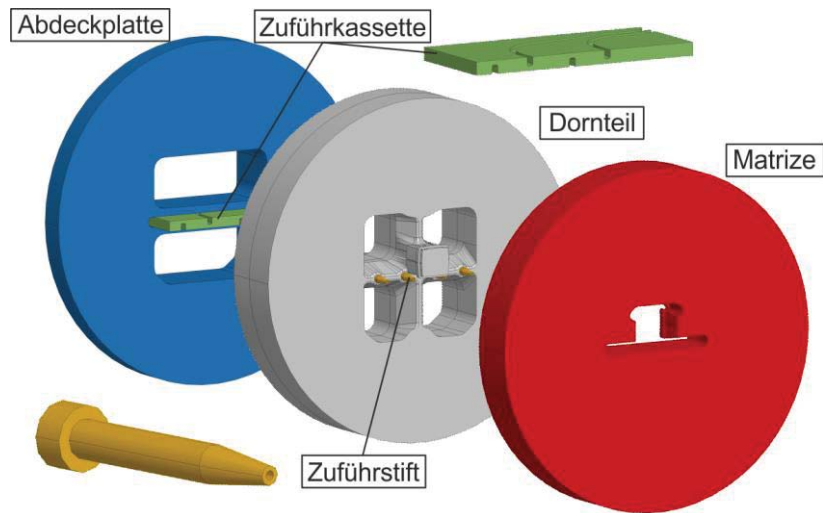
Werkzeugkonzept für die Erprobung mit der Institutspresse
